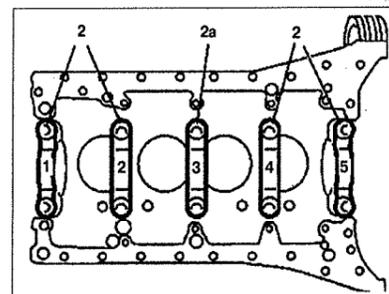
Маркировка крышек коренных подшипников коленчатого вала.
